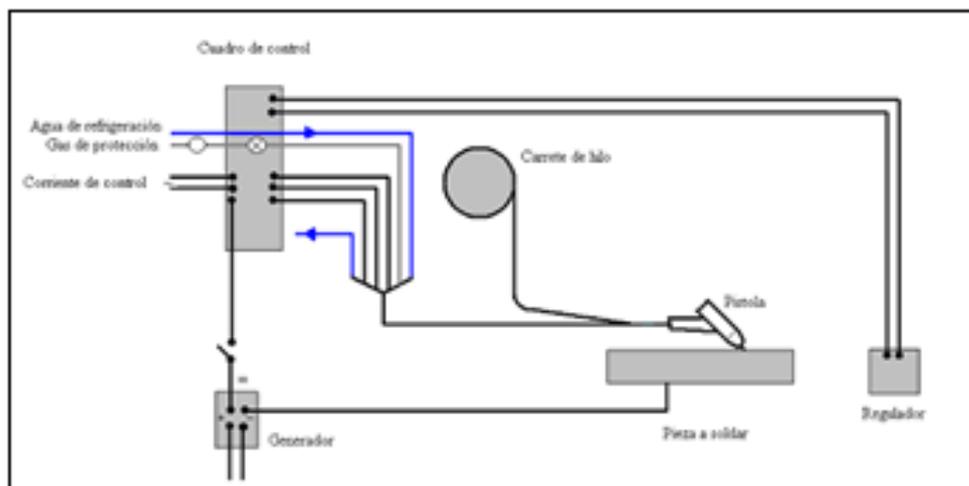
Instalación del proceso de soldadura MIG/MAG.
